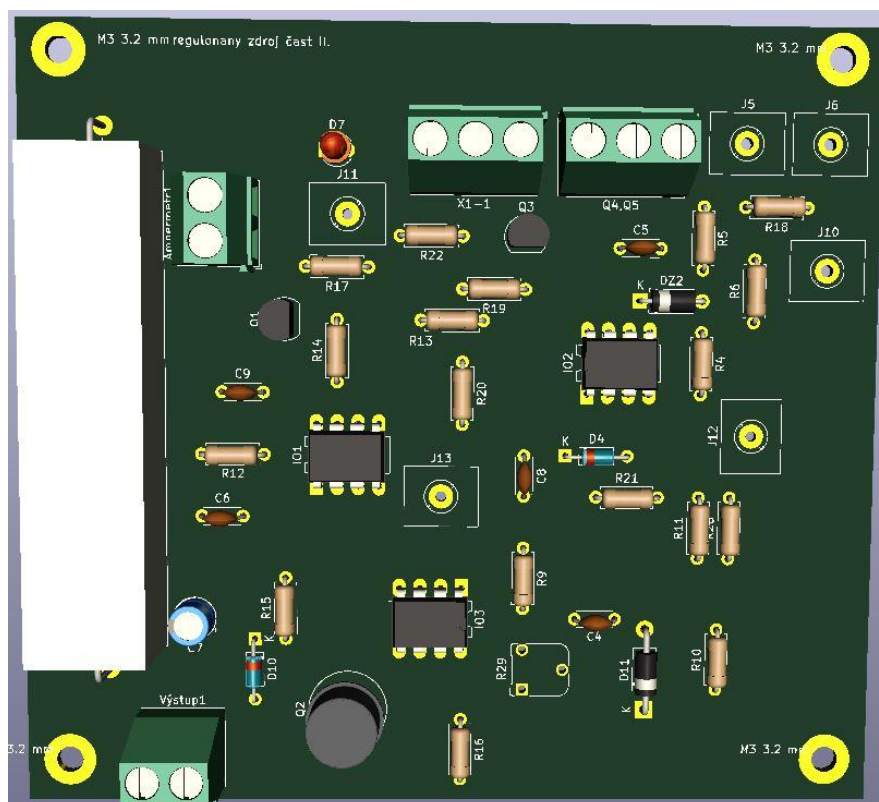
3D návrh desky stabilizovaného zdroje
